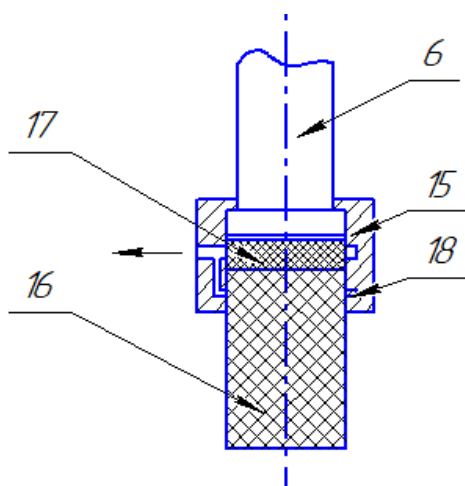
Устройство захвата с таблеткой и пресс-формой
